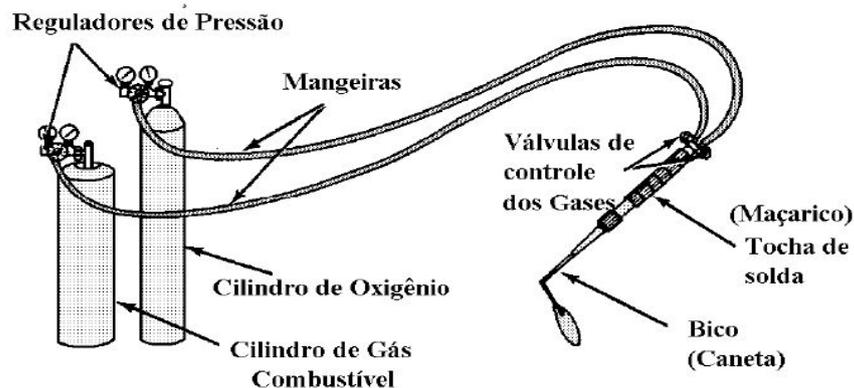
conjunto oxiacetilénico. Fonte - UTFPR
